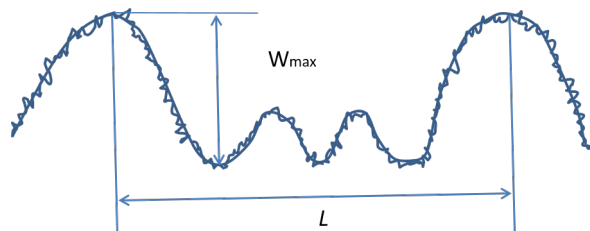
Схематичный вид поверхности с волнистостью и шероховатостью. Шаг волны равен L . Высота волны W_{\max} .
